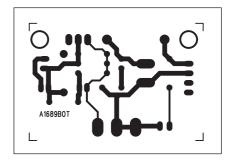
Obrazec desky spojů napájecího zdroje (strana TOP)
